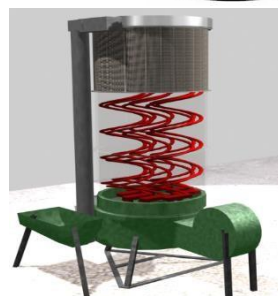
Зернова сушарка із спіралеподібними активаторами шару зерна
